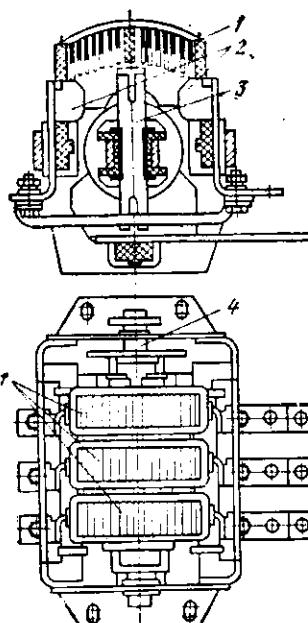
Блокировочный реверсирующий разъединитель:
